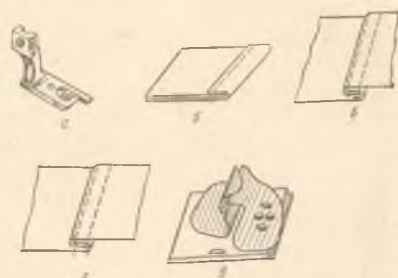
Лапка-запошиватель и приспособление для выполнения шва взамок
